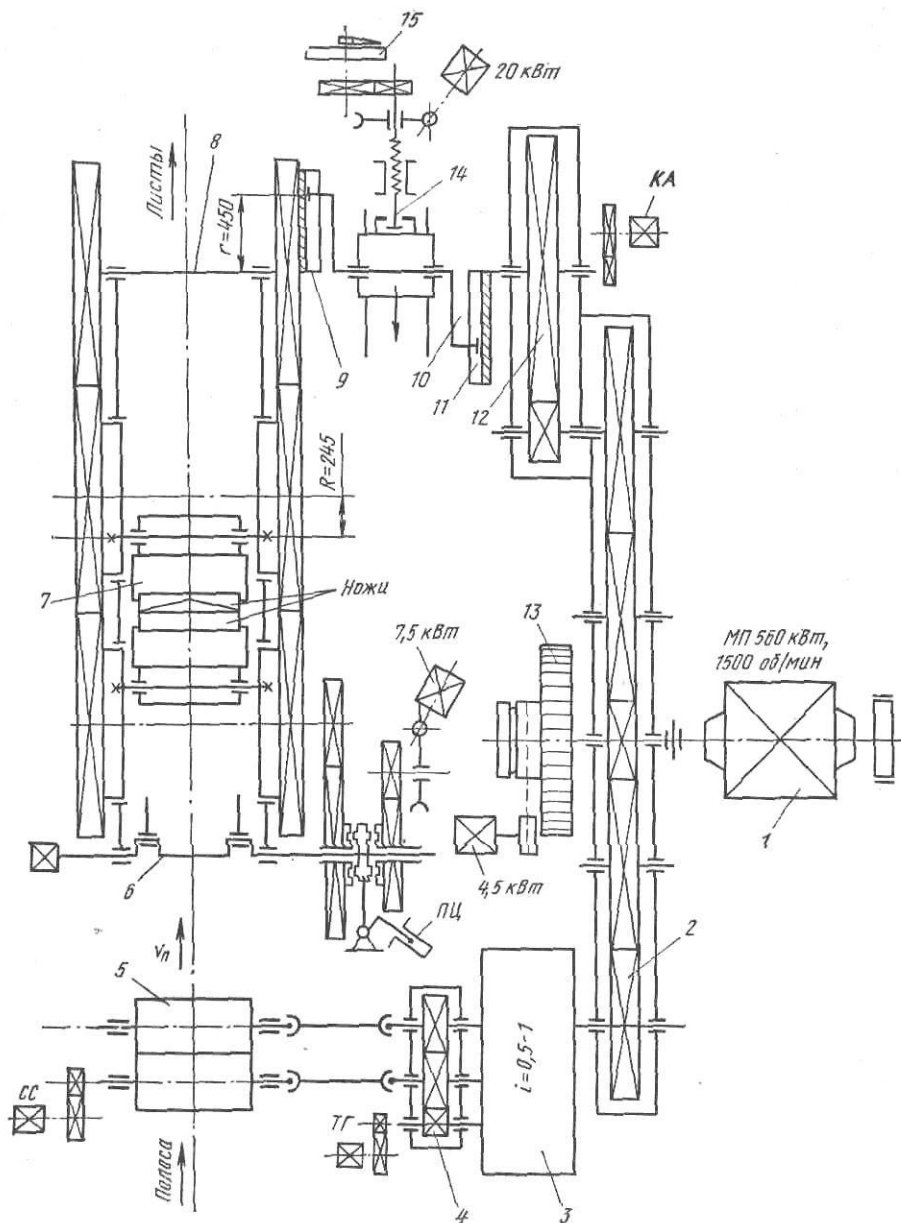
Кинематическая схема привода ленточных ножниц со скользящей штангой:
